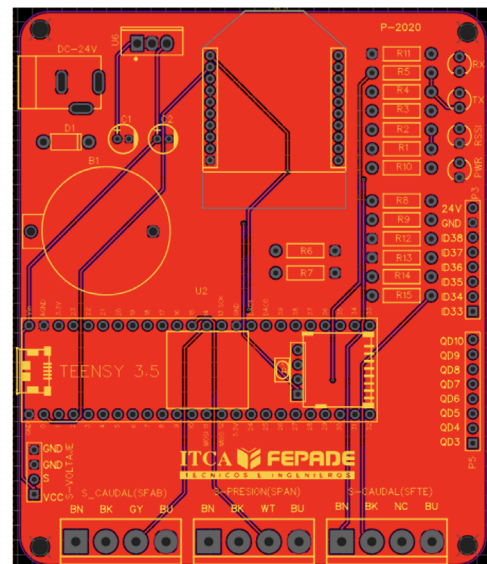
PCB de la tarjeta para la lectura de sensores de presión y caudal.
